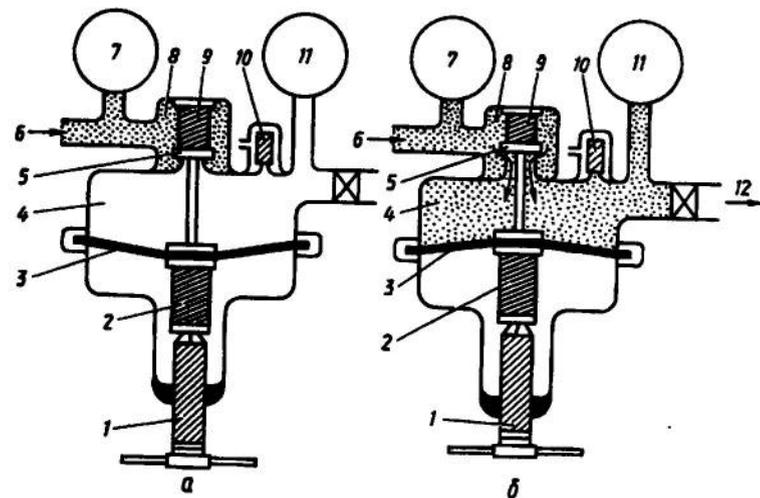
Схема роботи однокамерного газового редуктора:
